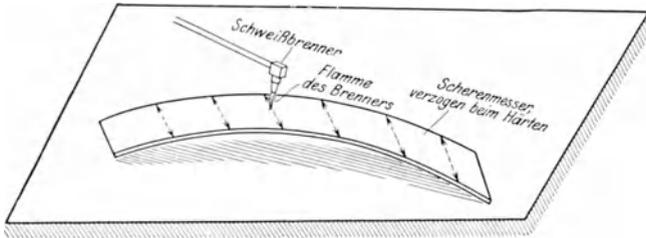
Richten eines Scherenmessers mittels Schweißbrenners.
